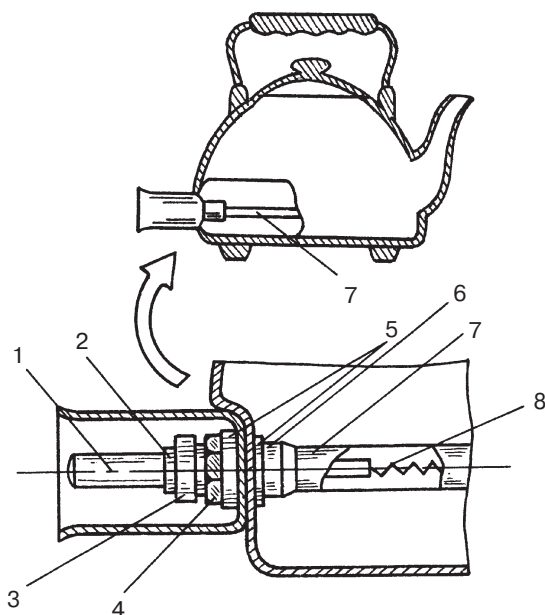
Ремонт электрического чайника: 1 — контактный штифт; 2 — шайба; 3 — фарфоровая колодка; 4 — гайка; 5 — резиновые сальники; 6 — штуцер; 7 — керамический изолятор; 8 — спираль
